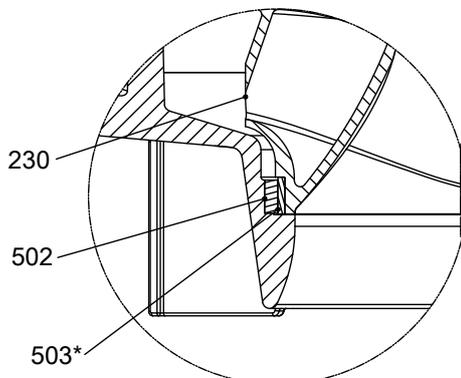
Ausführung mit Spaltring und Laufring (optional)
